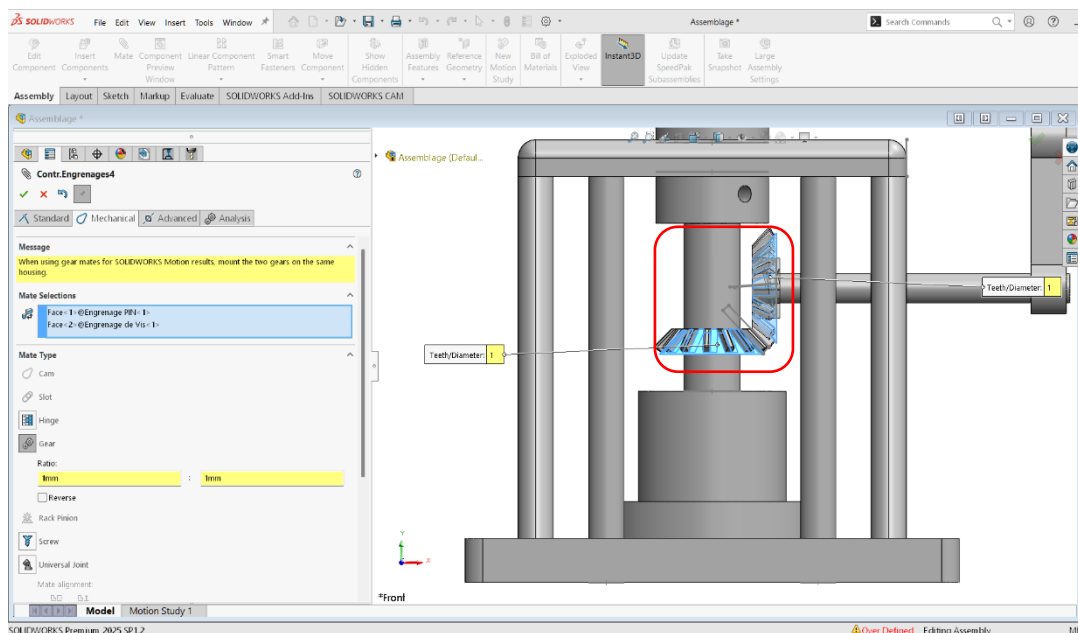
Assemblage et positionnement de l'engrenage conique sous SolidWorks.
